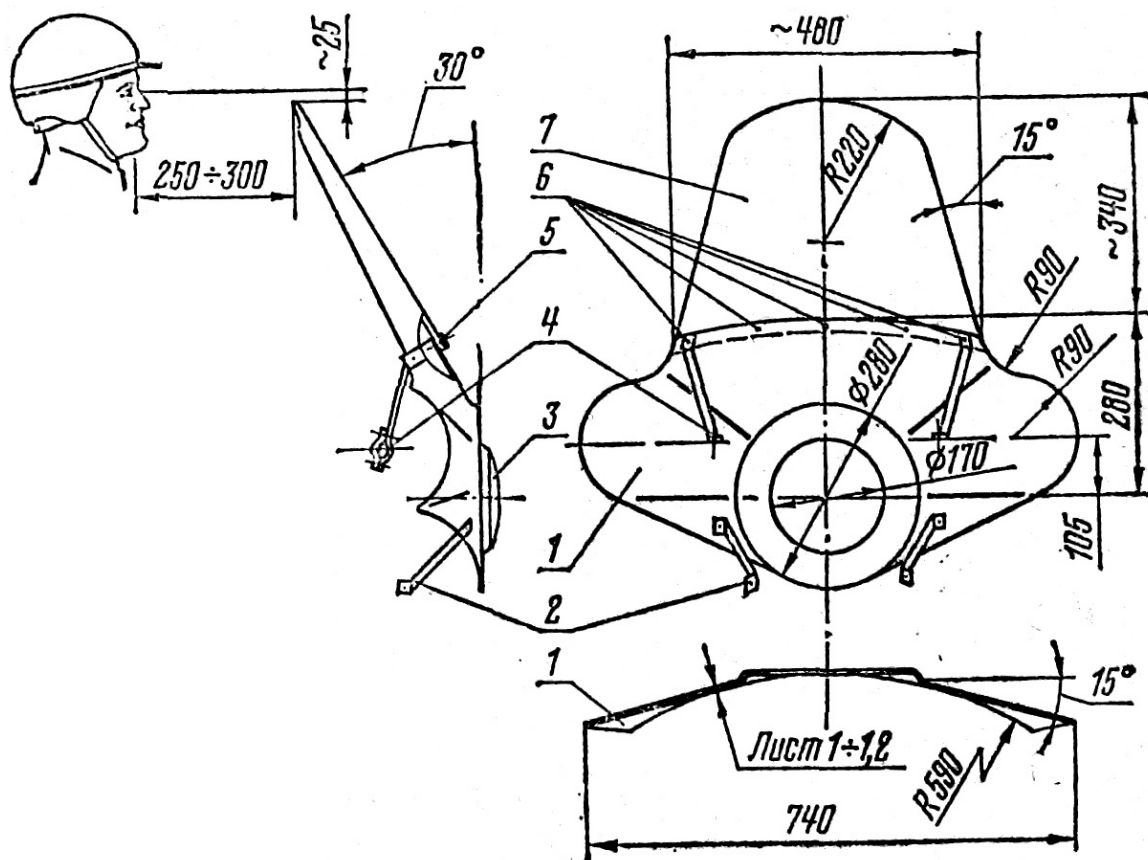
Ветровой щиток (вариант): 1 — основание (показана выдавка для рук); 2 — нижние кронштейны (крепление к стяжным болтам нижнего мостика или к кронштейну фары); 3 — фара; 4 — верхние кронштейны (крепление к трубе руля, стяжным болтам кронштейнов руля или к гайкам перьев вилки); 5 — металлическая накладка (ширина 30 мм); 6 — точки крепления стекла; 7 — прозрачная часть щитка из органического стекла
